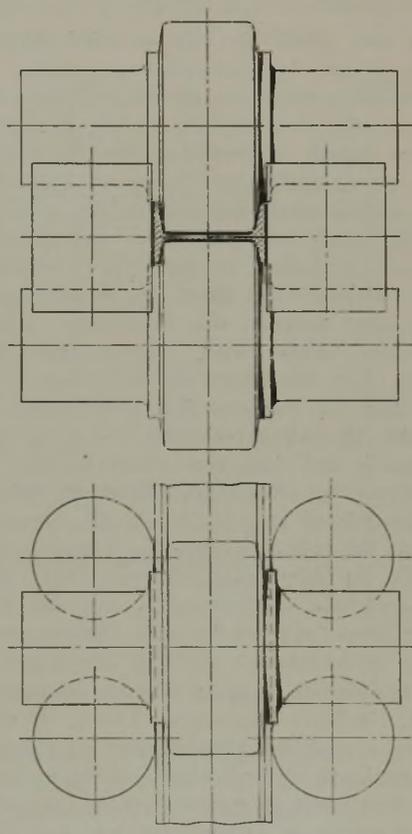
Blockwalzgerüst mit zylindrischen lotrechten Walzen.
